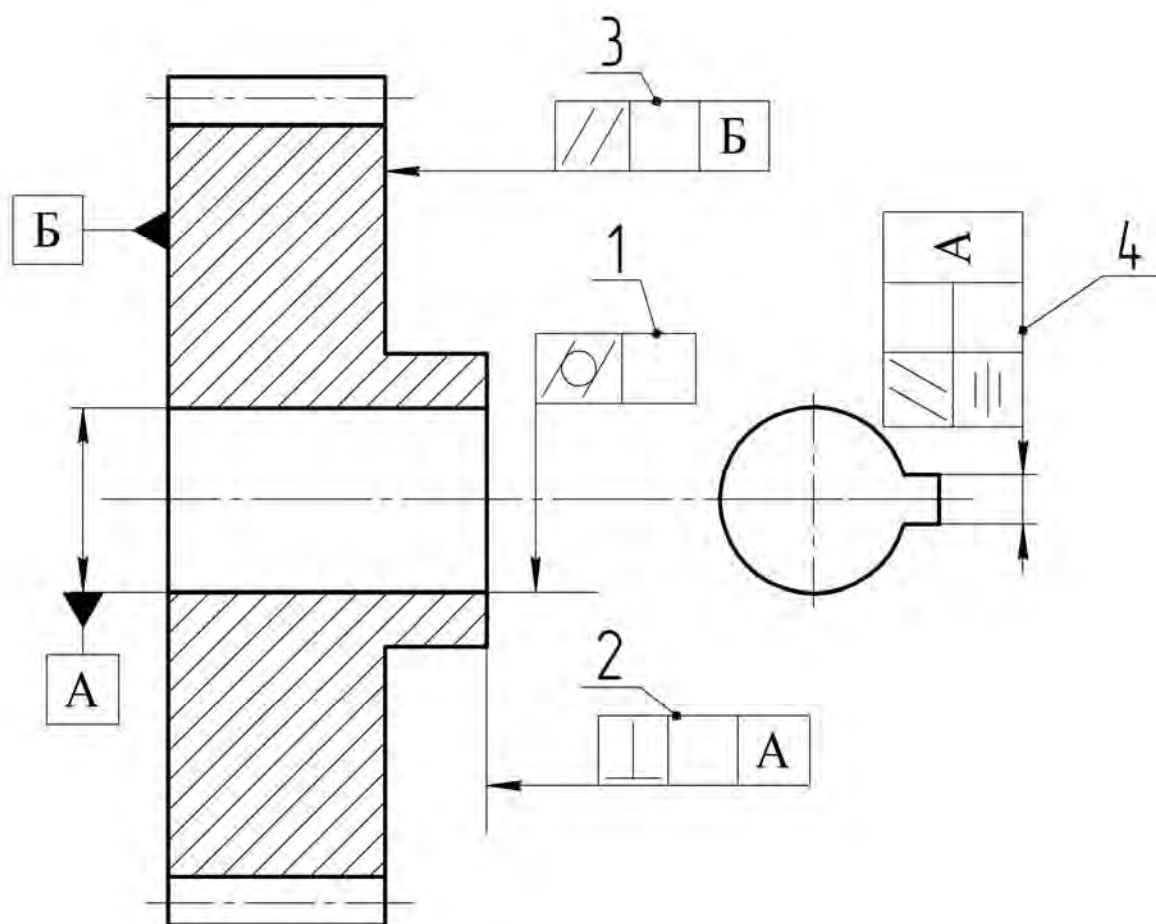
Допуски формы и расположения поверхностей колеса
